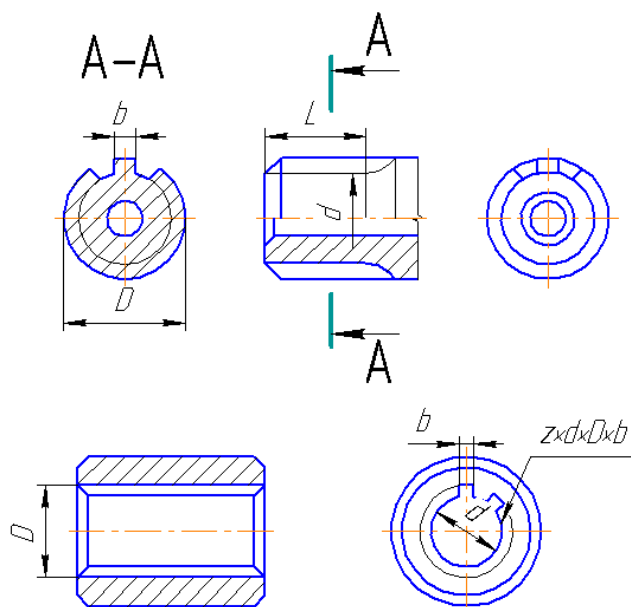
Пример детали со шлицевым хвостовиком и фрагменты чертежей деталей
